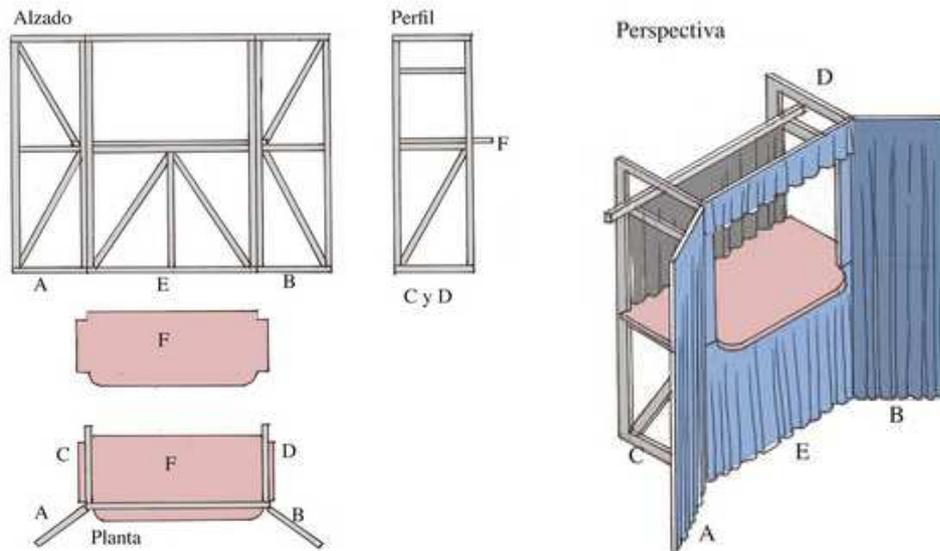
Alzado, planta, perfil y representación en perspectiva del teatrillo
